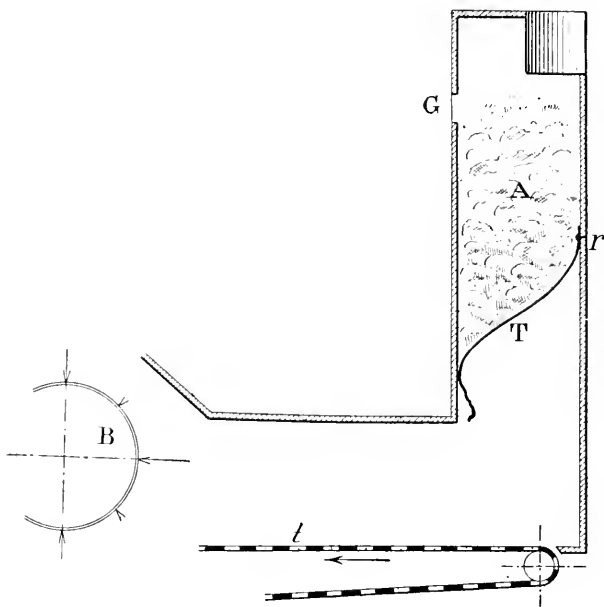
COUPE DU CONDUIT, OU CAISSE D'ALIMENTATION
